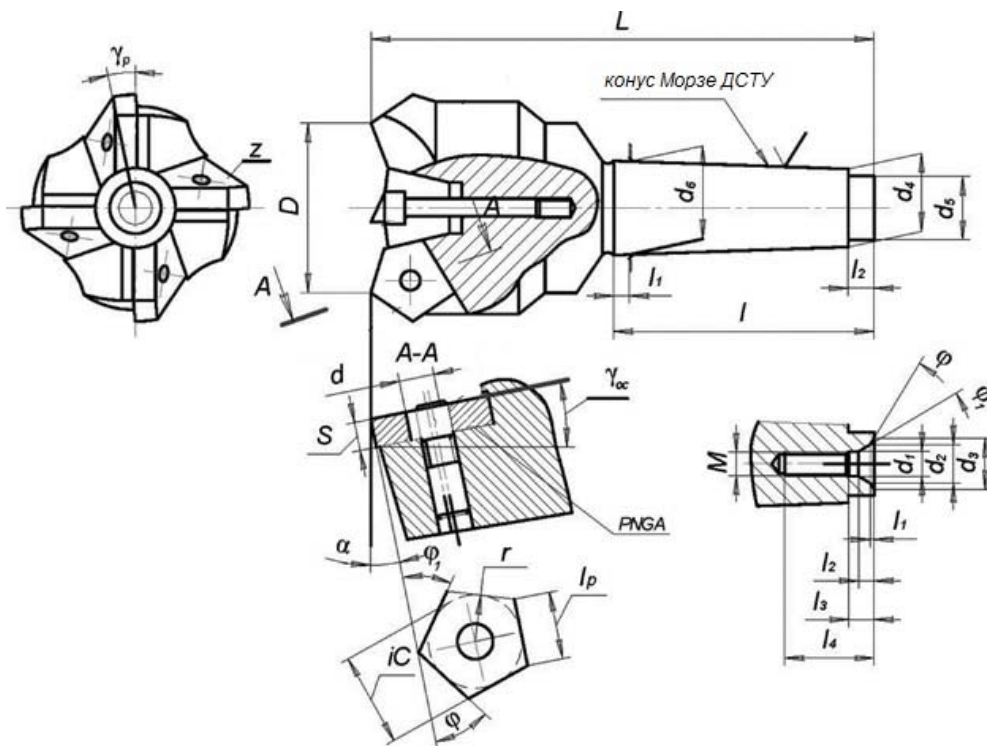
Фреза кінцева, оснащена п'ятигранними твердосплавними пластинами
